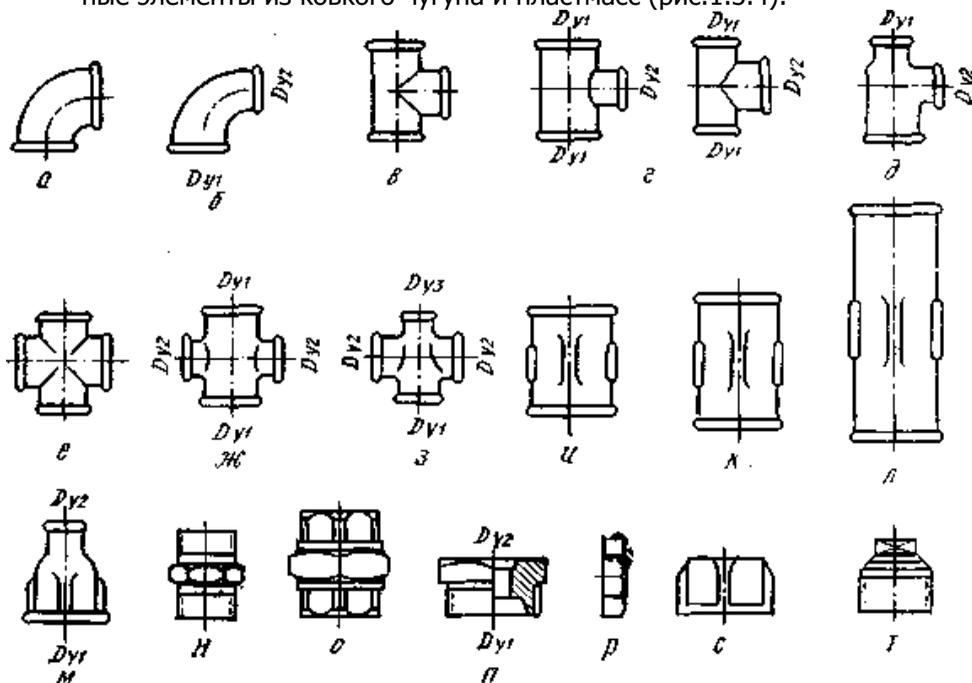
Соединительные детали из ковкого чугуна для трубопроводов: а – угольник прямой; б – угольник переходный; в – тройник прямой; г – тройник переходный, д – тройник с двумя переходами; е – крест прямой; ж – крест переходный; з – крест с двумя переходами; и – муфта короткая; к – муфта прямая длинная; л – муфта компенсирующая; м – муфта переходная; н – ниппель двойной; о – гайка соединительная; п – футорка; р – контргайка; с – колпак; т – пробка
